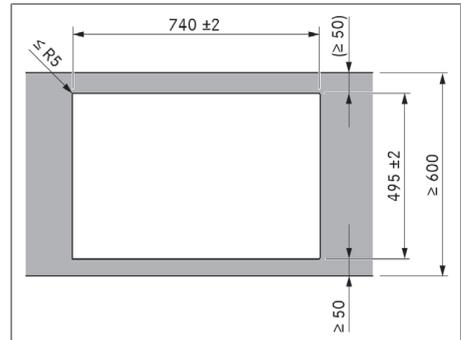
Medidas de recorte para montagem por sobreposição
